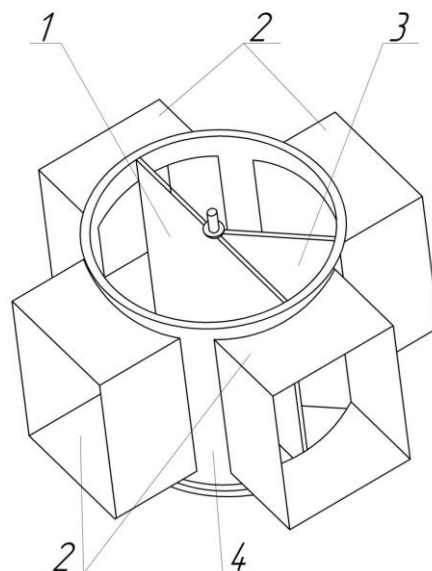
Конструктивно-технологічна схема повітрообмінника: 1 – рухома заслінка; 2 – патрубки; 3 – нерухома заслінка; 4 – циліндричний корпус (камера змішування)
